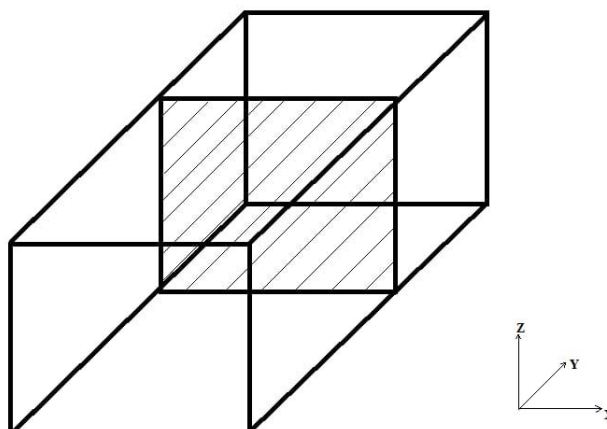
Схема расположения образца для металлографических исследований в теле заготовки
